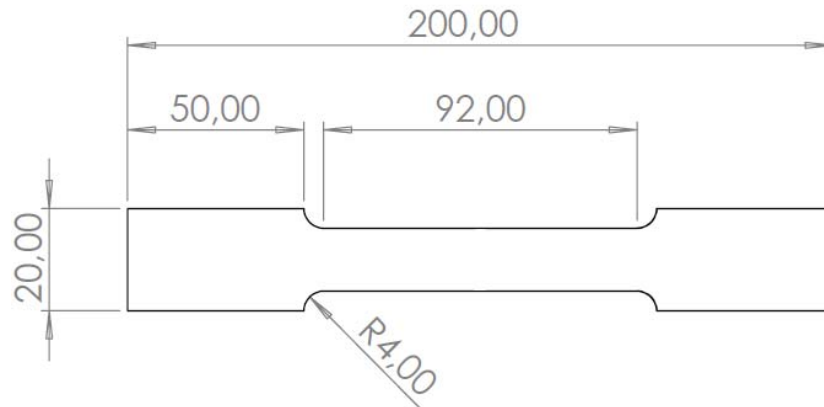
Corpos de prova de tração soldado (Dimensão em milímetros).
